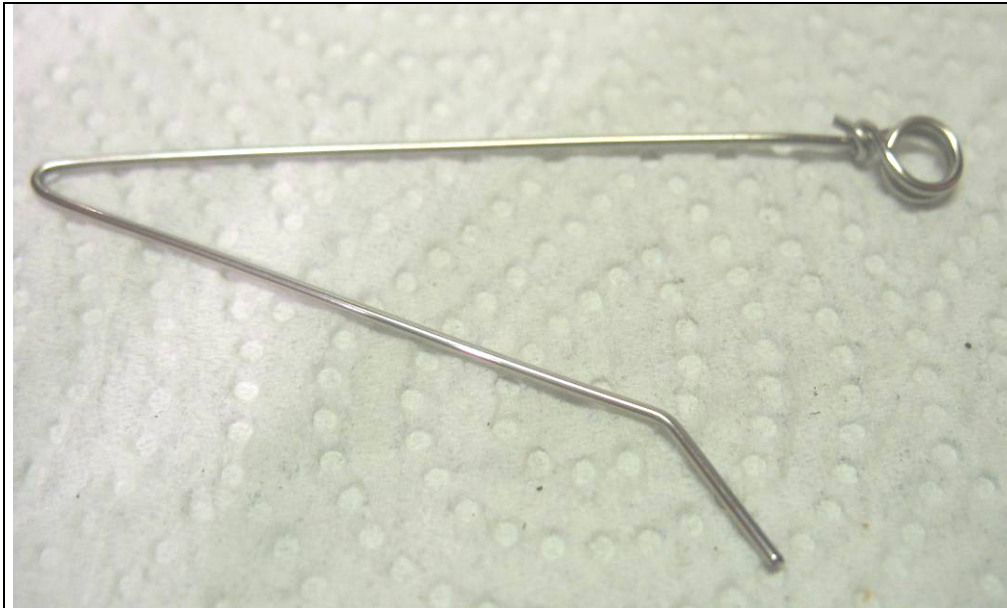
das Drahtende umgelegt, der Draht abgelängt und die V-Feder geformt.
